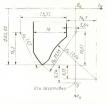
Профиль дисковой фрезы для обработки канавок под винтовые пластинки из твердых сплавов
